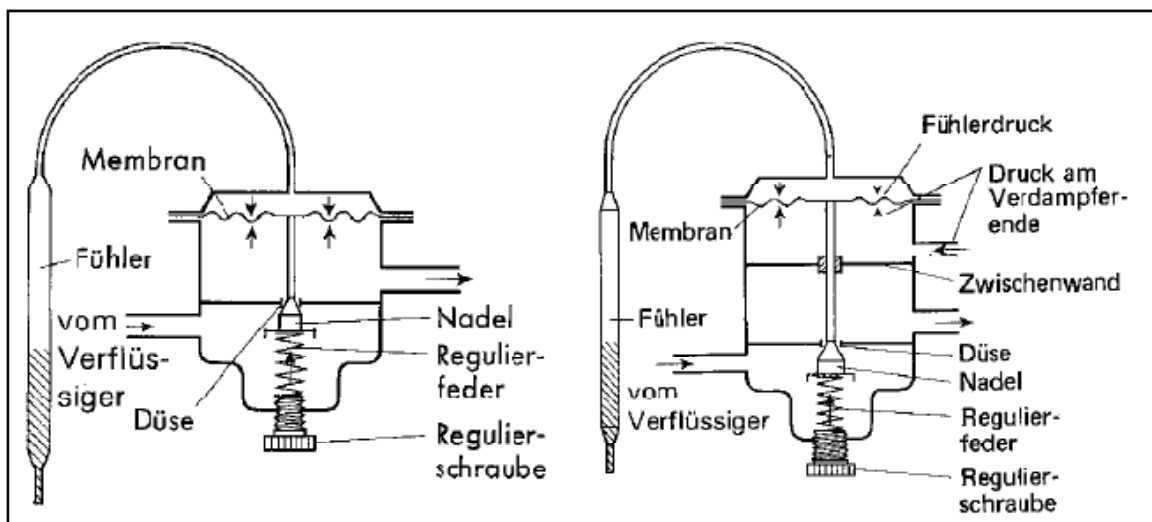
Thermisches Expansionsventil mit inneren (links) und äußerem (rechts) Druckausgleich²
